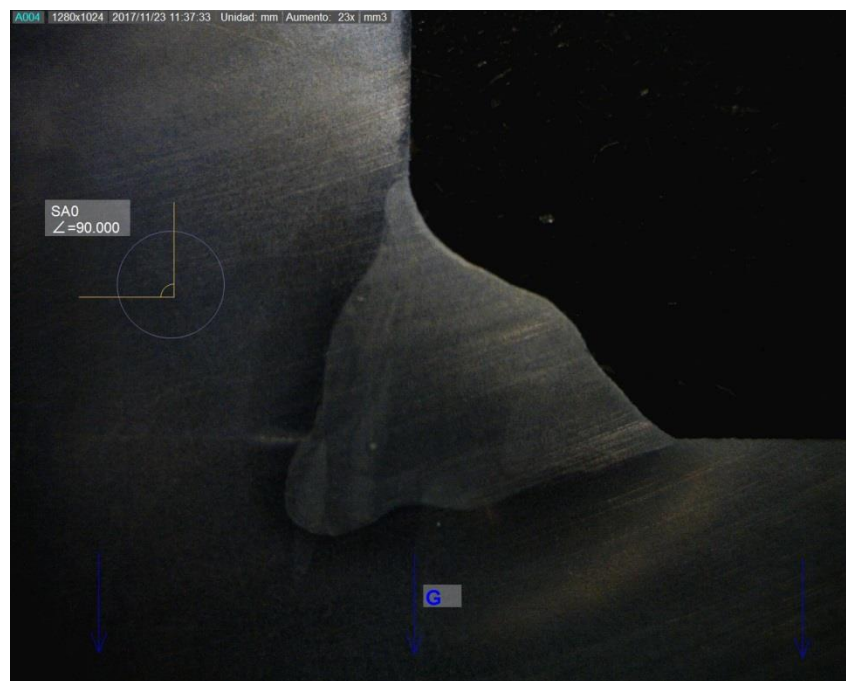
2 Perfil obtenido en cupón de soldadura 1B.
